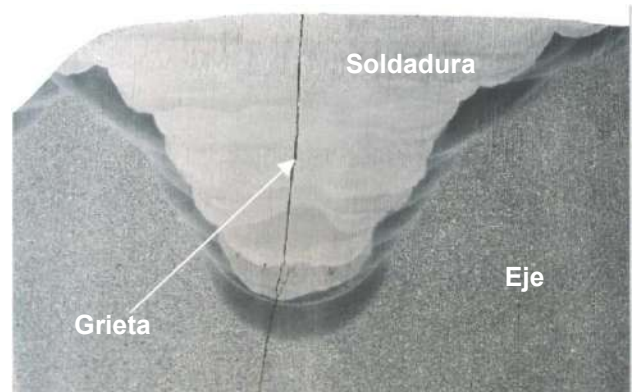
Corte transversal de eje recuperado por soldadura deficiente, con grieta iniciada en la soldadura y, en otra posición, fractura iniciada en la ZTA.
